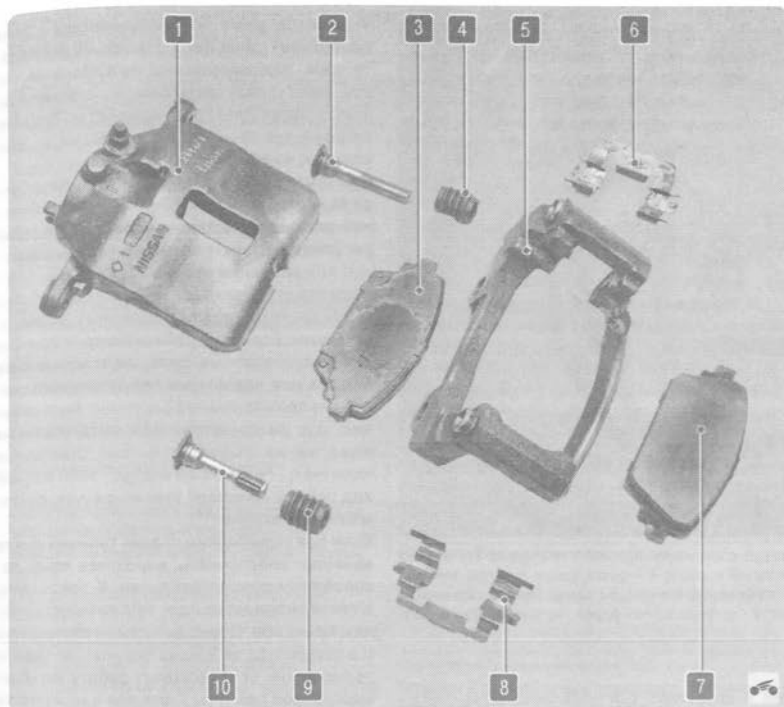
Детали переднего тормозного механизма: 1 – суппорт; 2 – верхний направляющий палец суппорта; 3 – внутренняя тормозная колодка; 4, 9 – защитные чехлы направляющих пальцев; 5 – направляющая тормозных колодок; 6, 8 – фиксирующие пружины; 7 – наружная тормозная колодка; 10 – нижний направляющий палец суппорта
